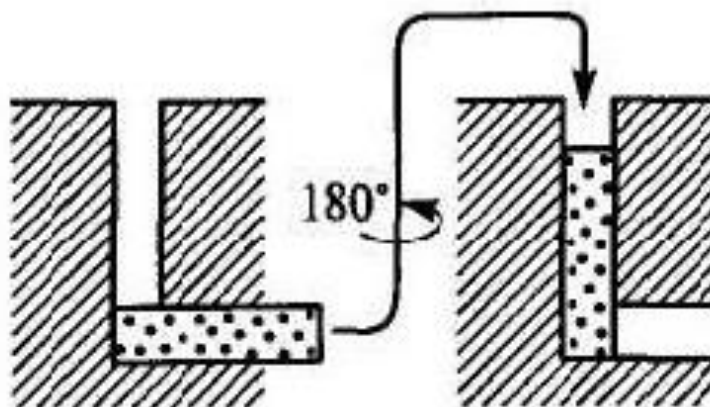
Поворот заготовки на угол  $180^\circ$
